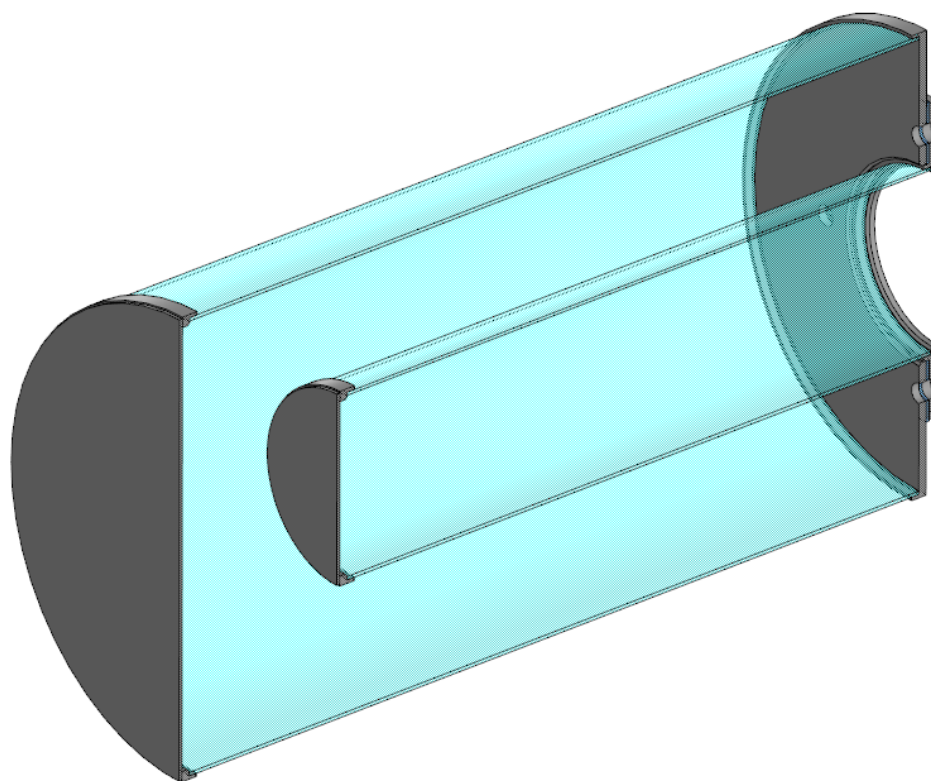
Модель осесимметричного фильтрующего элемента с фильтрующей загрузкой
